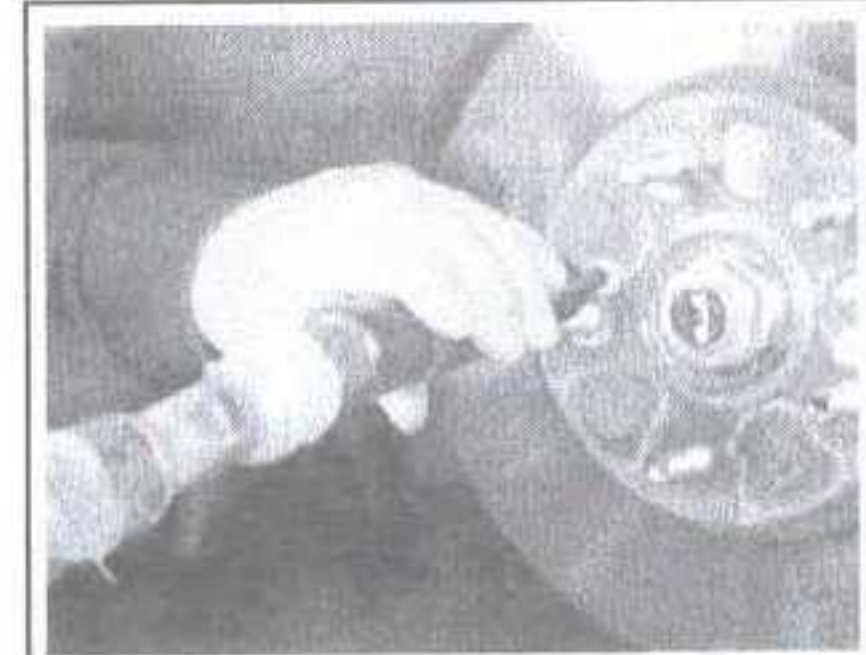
Для откручивания крепежных винтов тормозного диска может потребоваться ручной гайковерт ударного действия
